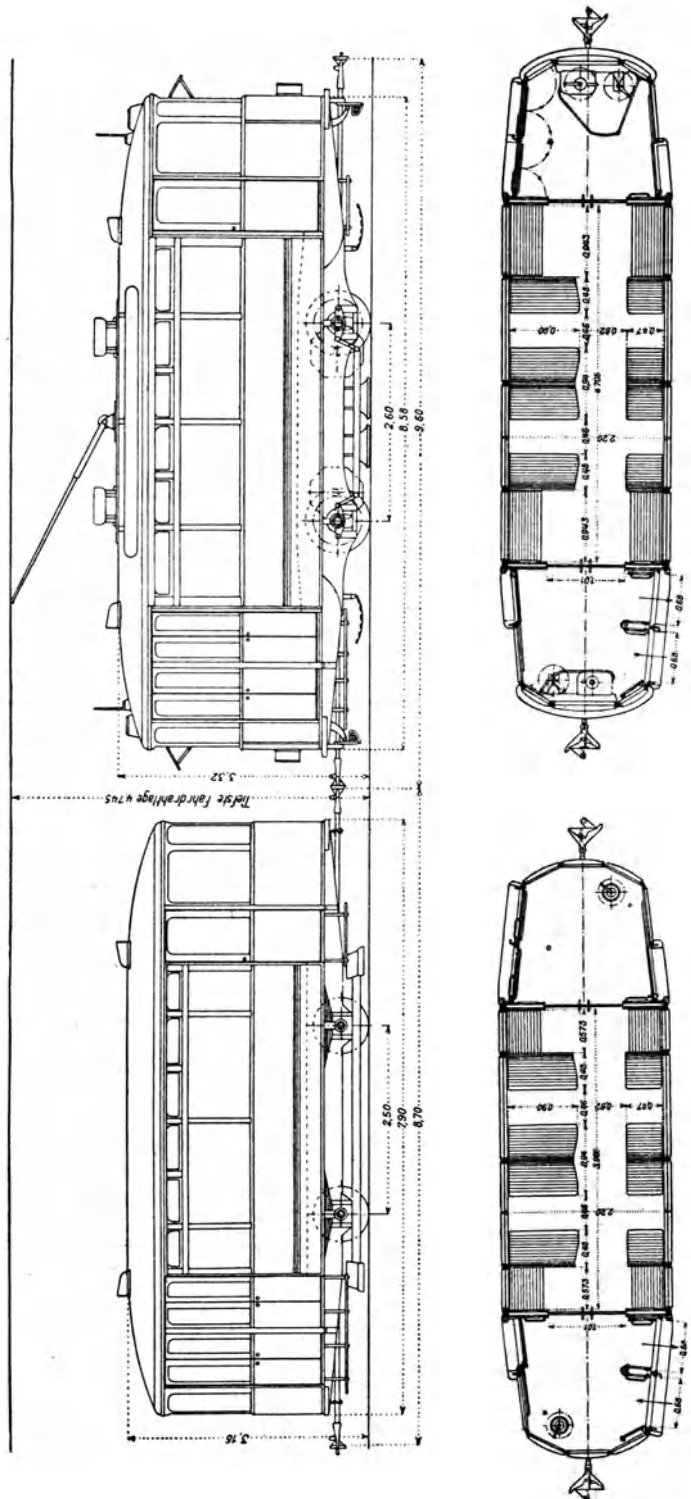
Ansicht und Grundriß eines Trieb- und eines Anhängewagens der Züricher Straßenbahn, Tommendach, Quersitze.
